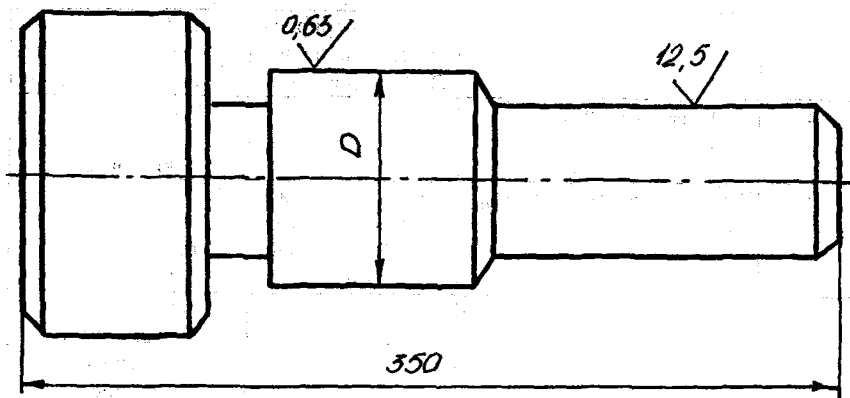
Вал ступенчатый (материал - группа стали M1 или M2; заготовка - штамповка на ГKM)
